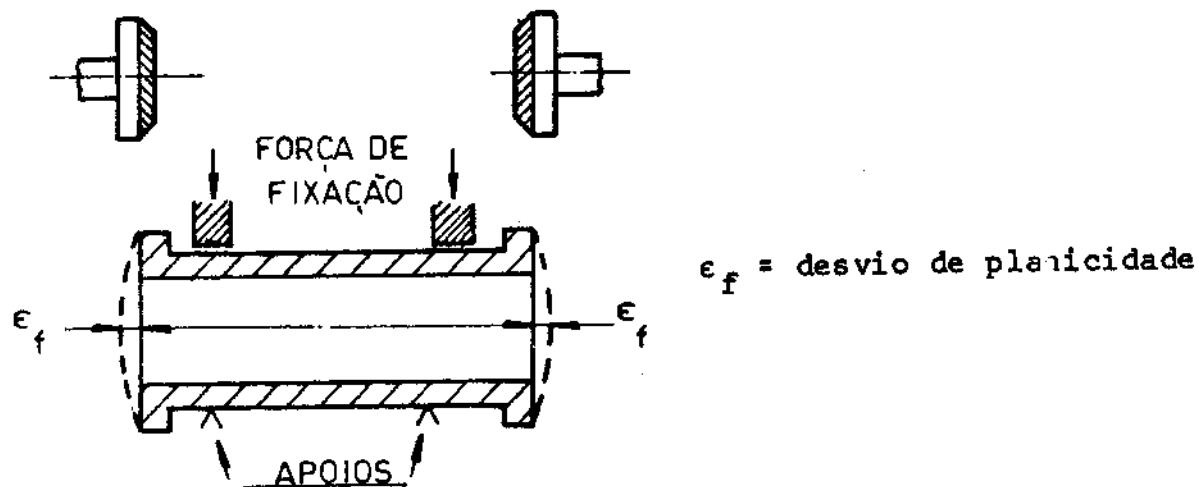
Desvio de fixação na usinagem de carcaças
